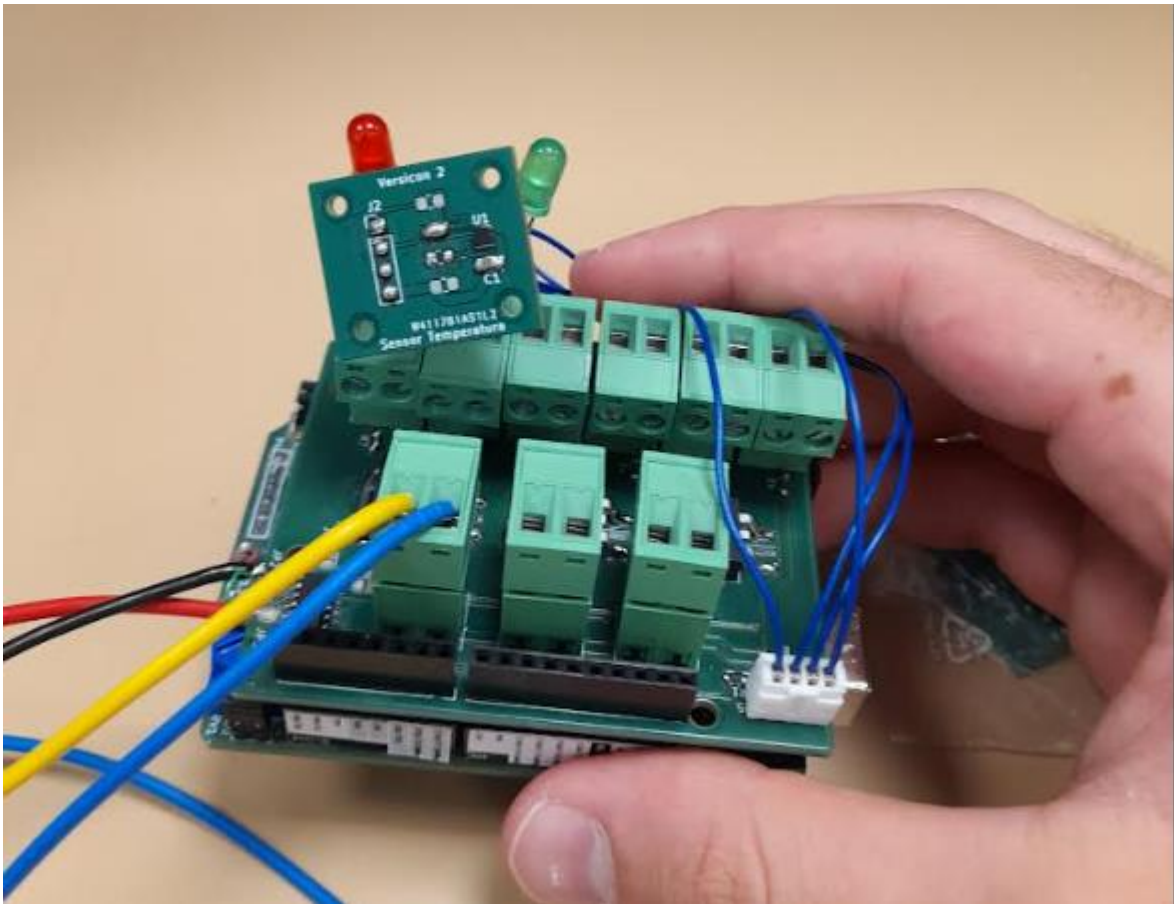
Proceso de soldado de la PCB
